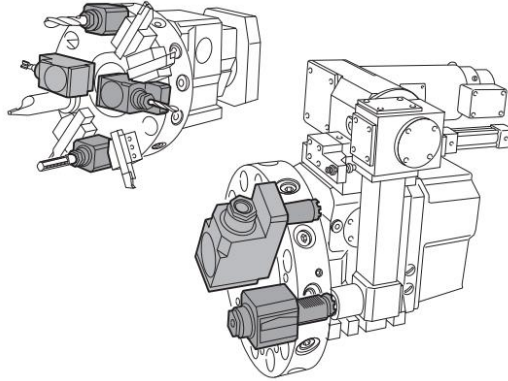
Револьверні головки з нерухожими і обертовими інструментами
